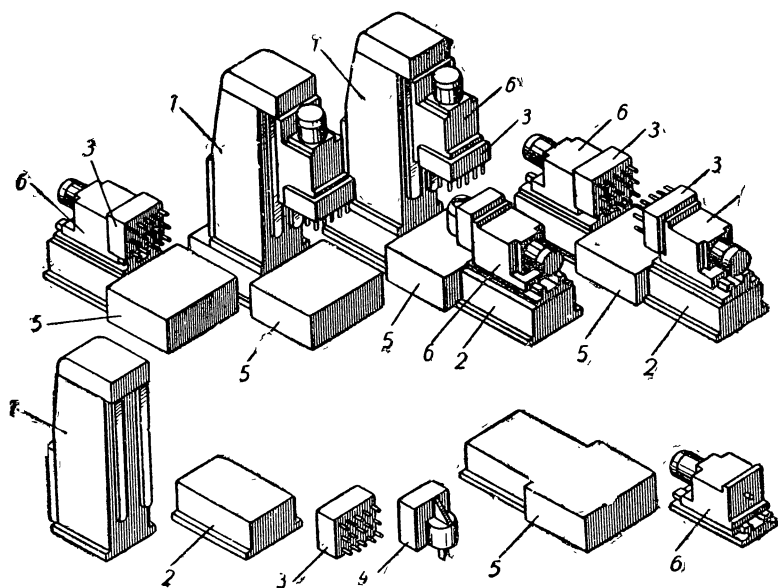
Схема компоновки многопозиционных агрегатных станков: 1 — колонна; 2 — подставка; 3 — шпиндельная коробка; 4 — фрезерная насадка; 5 — станина; 6 — силовая головка.
